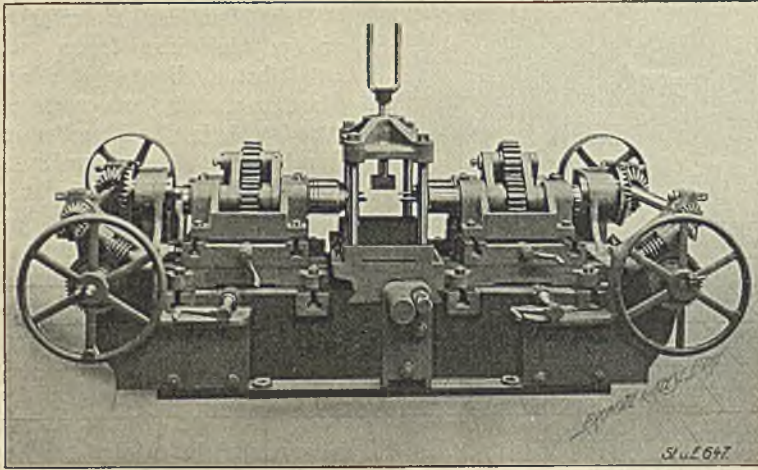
Vierspindel-Schienenbohrmaschine.
